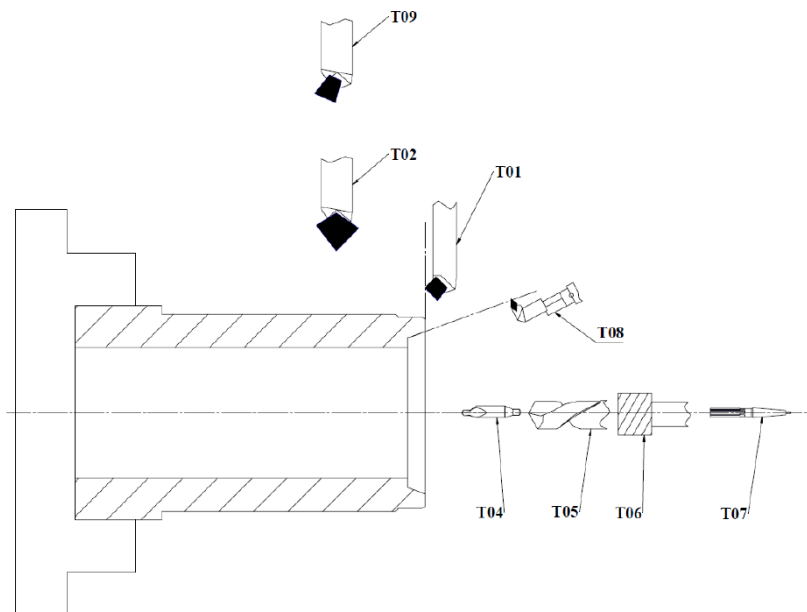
Plan obrade za grupnu operaciju struganjem 1 za kompleksni dio
